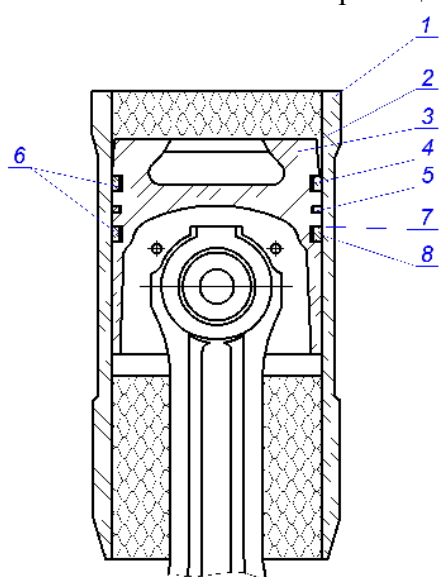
Циліндро-поршневий механізм двигуна внутрішнього згорання
